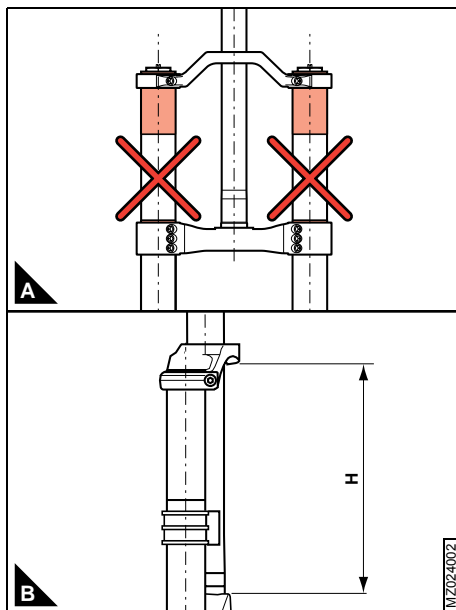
Installazione sul telaio forcelle a doppia piastra: (2A) Fissaggio piastre sterzo, (2B) Massimo sfilamento piastre
